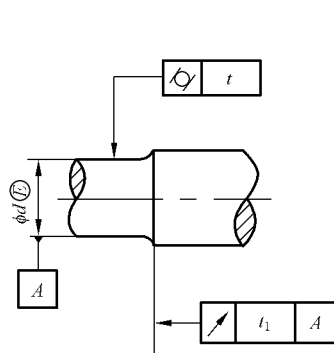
轴颈的圆柱度公差和轴肩的轴向圆跳动
